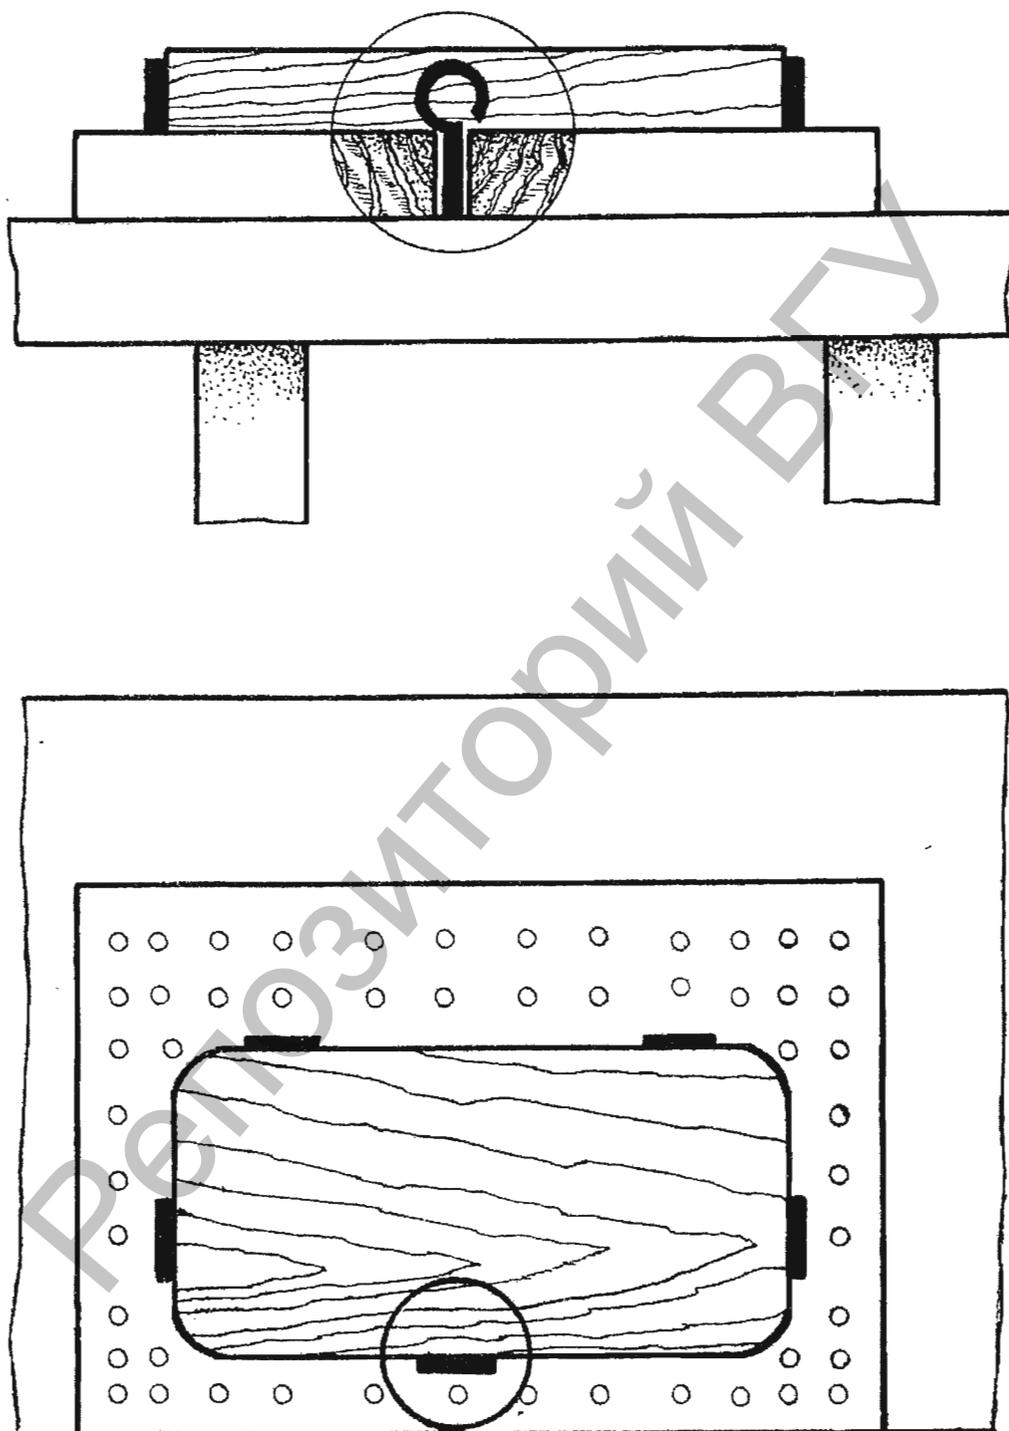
Крепление заготовки для резьбы при помощи специальной доски с модульными отверстиями.
